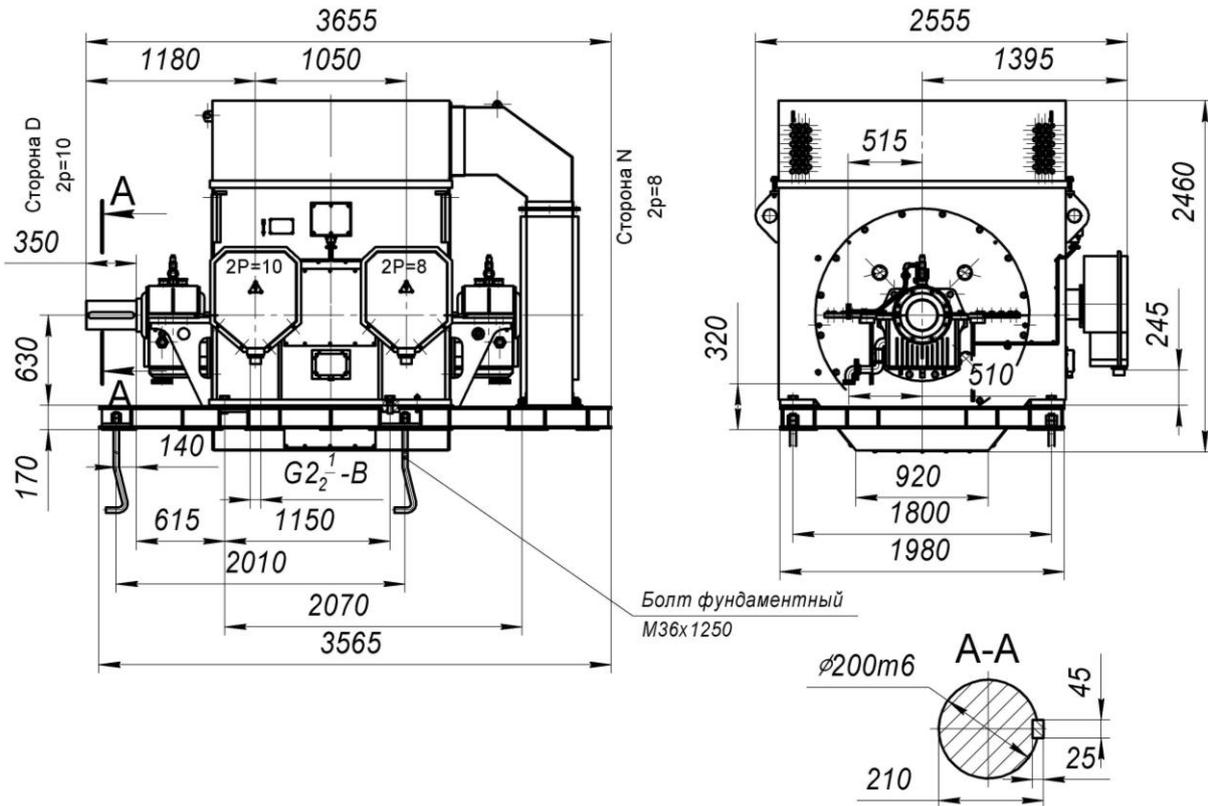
Габаритные и установочно-присоединительные размеры двигателя АОД-1250/800-8/10У1 (масса двигателя – 14610 кг)
